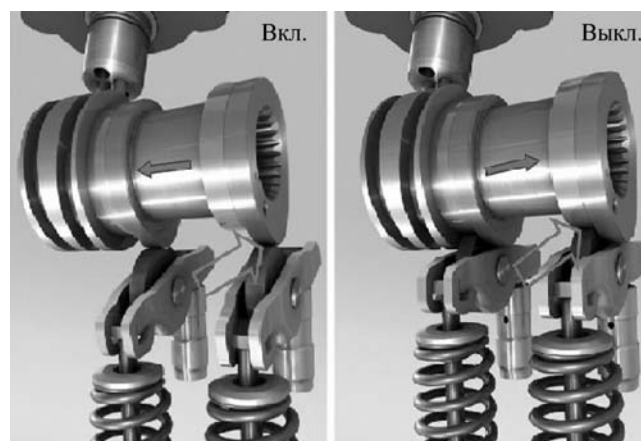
Профили кулачков распределительного вала двигателя "Фольксваген", оснащенного системой отключения цилиндров
